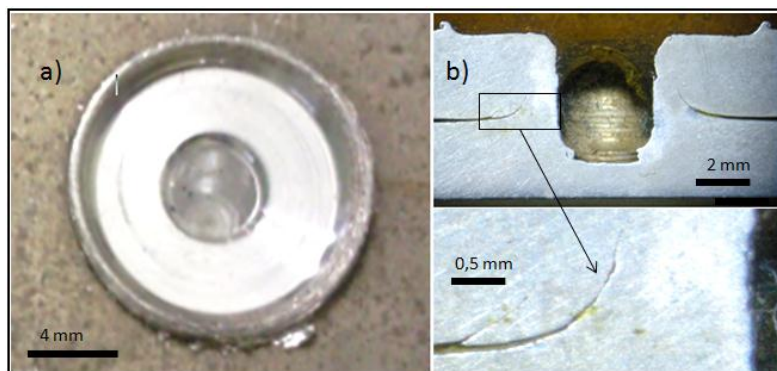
Punto de soldadura por la técnica de fricción-agitación a) Vista superior, b) Vista de la sección transversal
